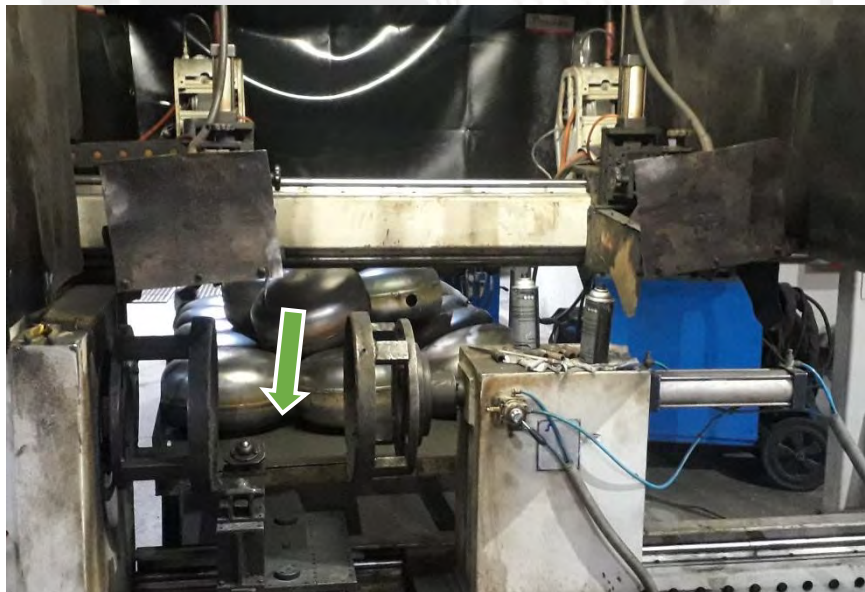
Parte inferior de máquina soldadora circunferencial
